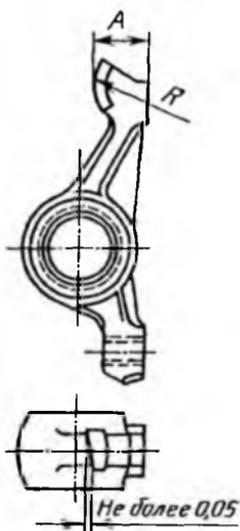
Схема рабочей поверхности бойка коромысла:
